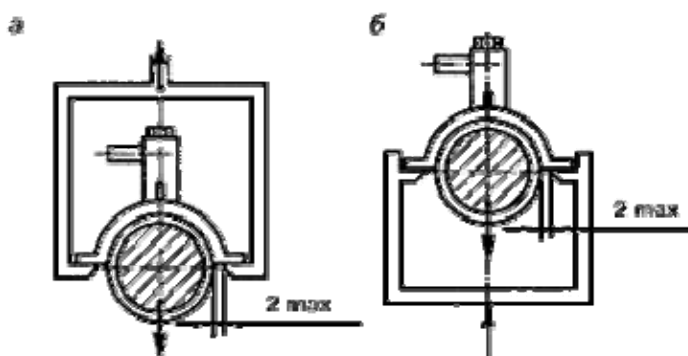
Схемы испытания седловых полиэтиленовых отводов на отрыв
